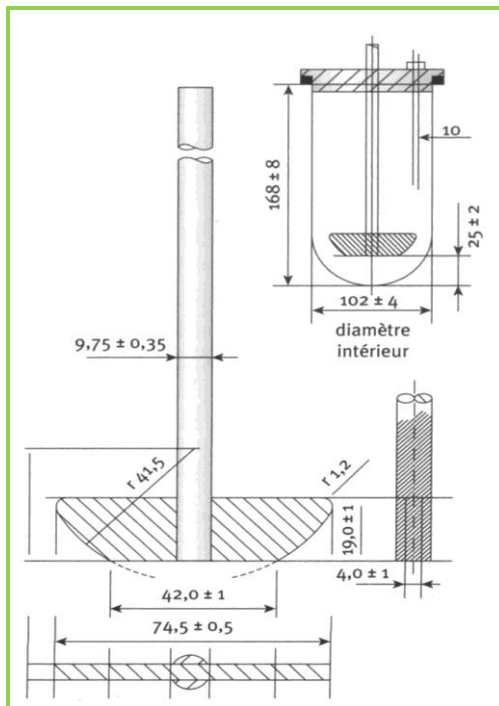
Appareil 2, à palette (dimensions en millimètres)
